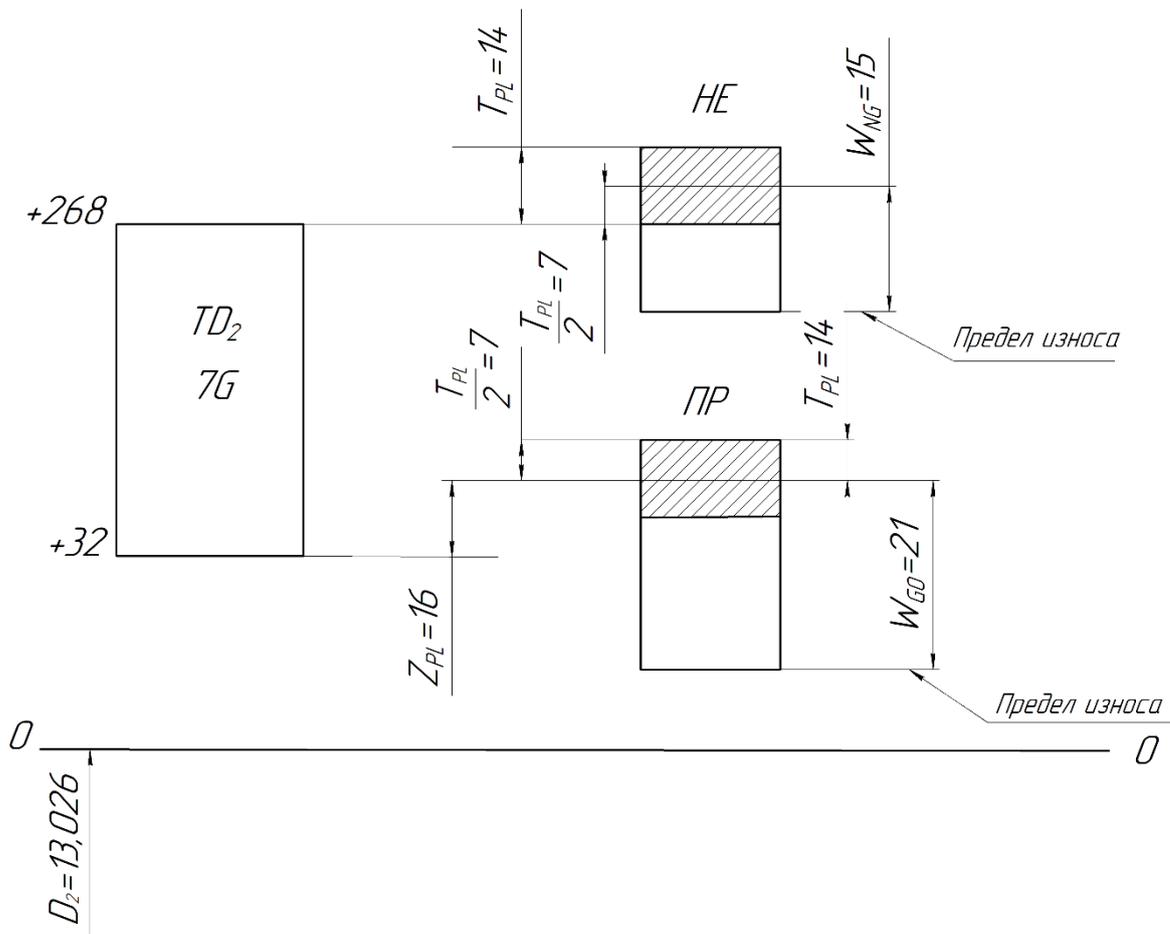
Схема расчета полей допусков резьбового калибра пробки по среднему диаметру
